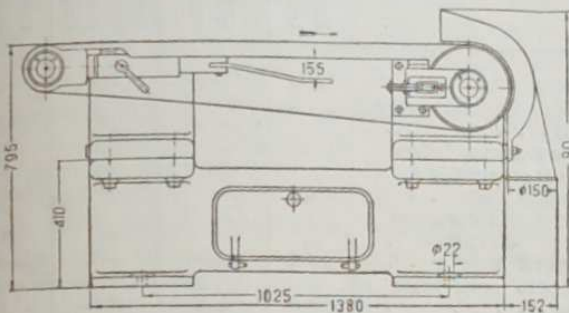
Шлифовально-ленточный горизонтальный станок с неподвижным столом
